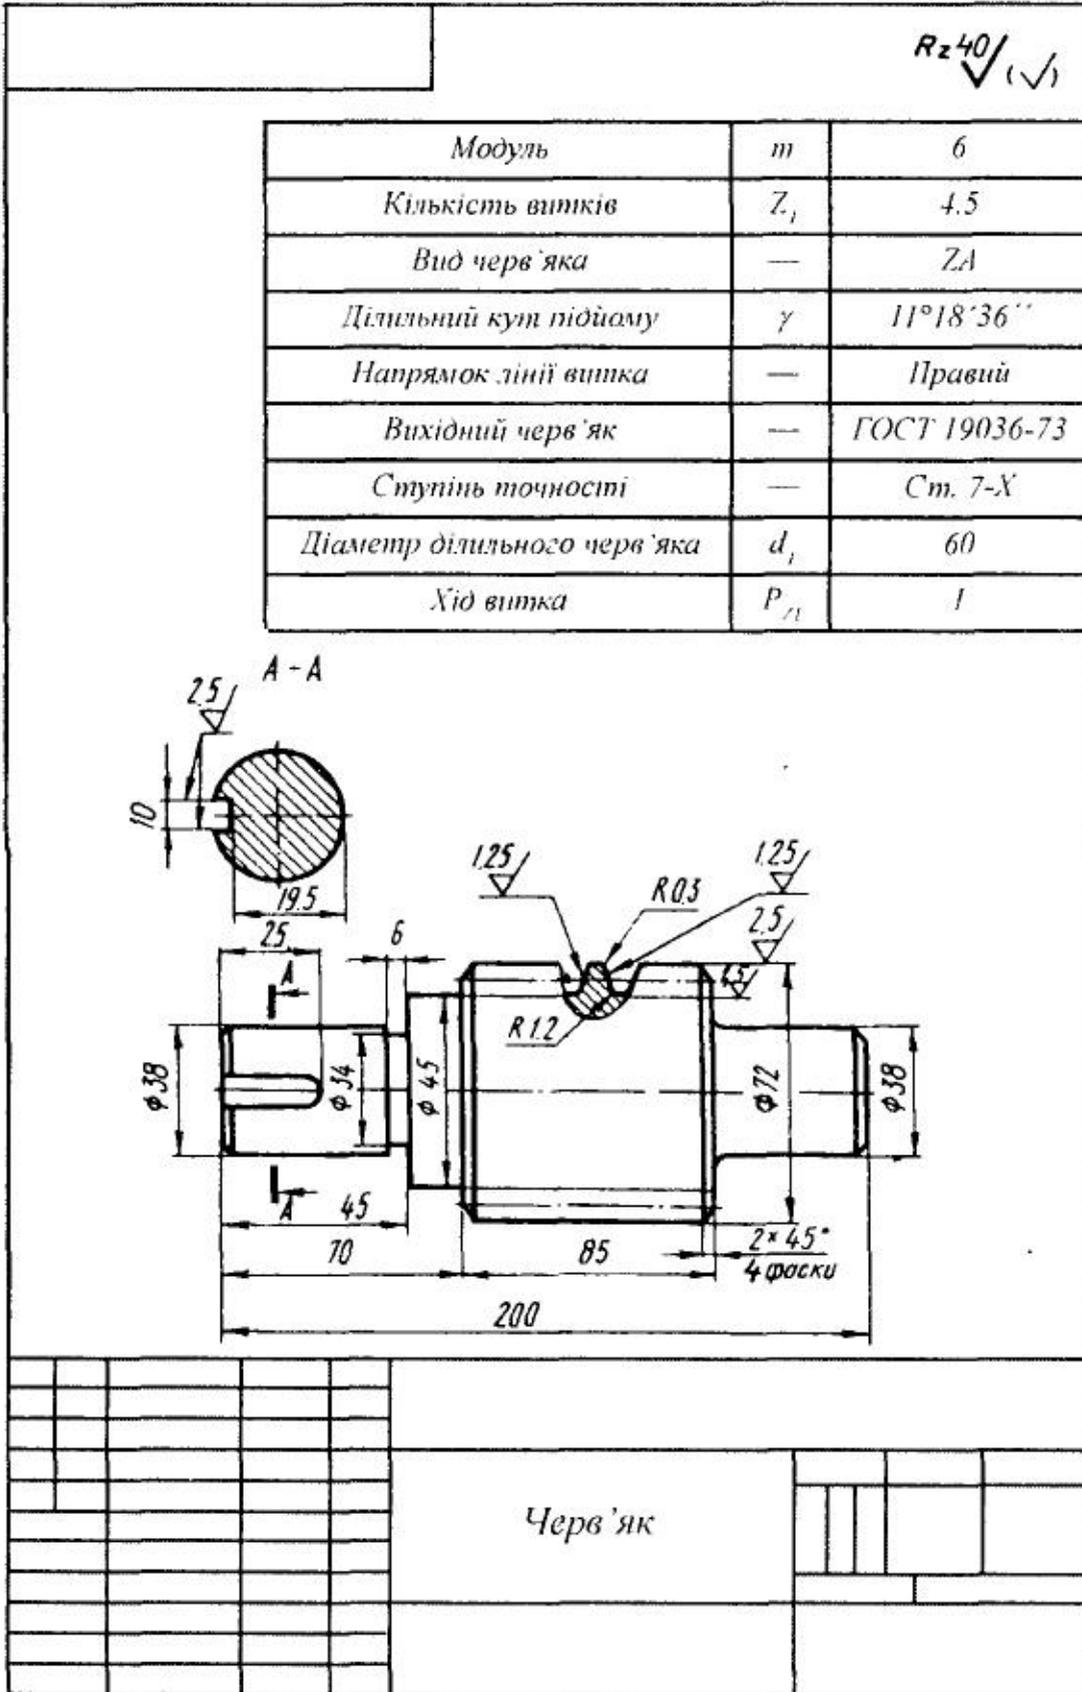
Креслення черв'яка черв'ячної передачі.
